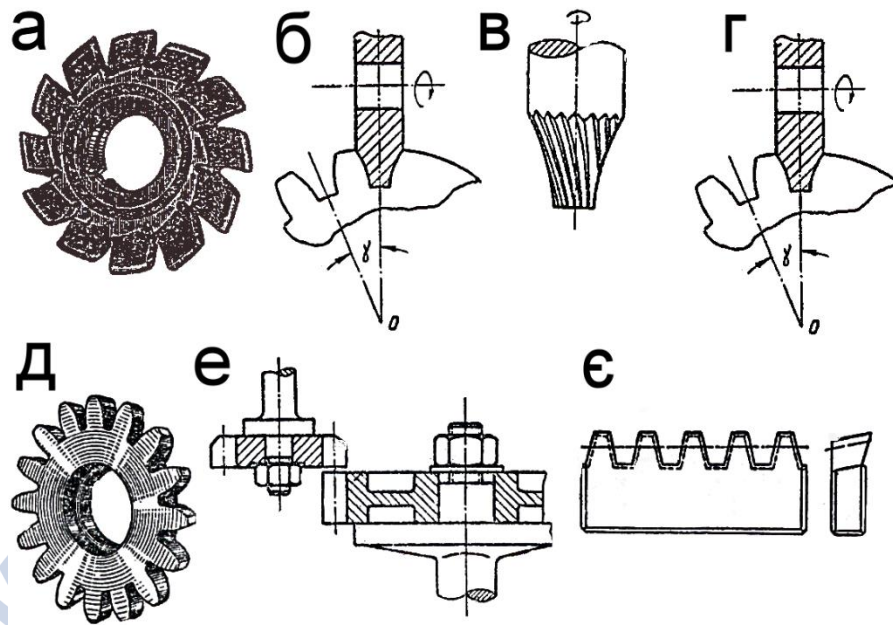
Способи виготовлення зубів зубчастих передач.
